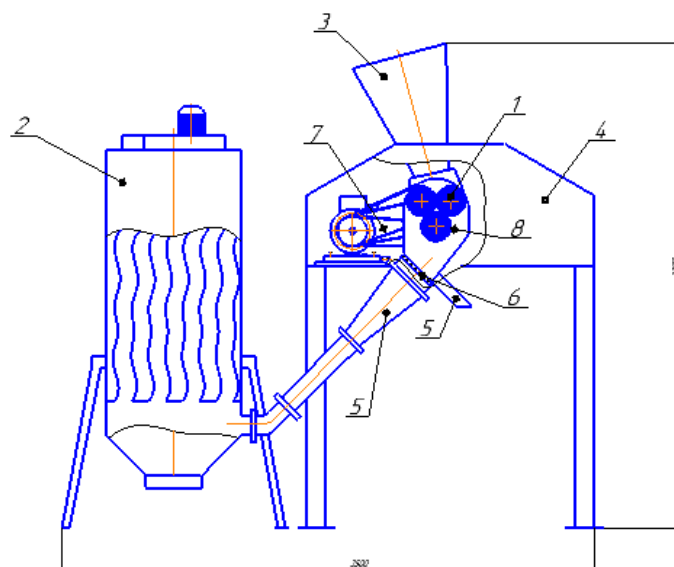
Установка для вторичной очистки корпусов помадных и желейных кондитерских изделий
